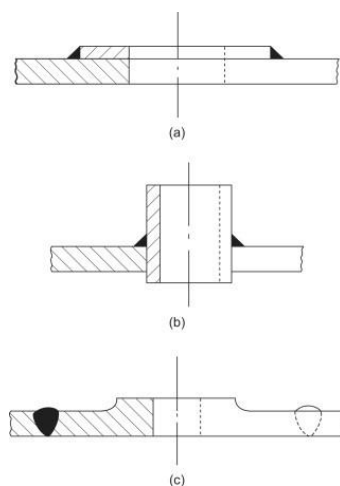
Tipos de compensación para aperturas: a) Almohadilla soldada b) Boquilla insertada c) Anillo forjado. Fuente: (1)
